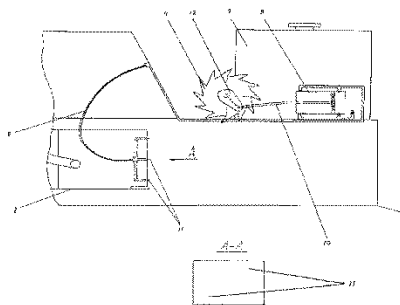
Схема устройства для обработки заготавливаемых кормов консервантами по патенту № 61079
